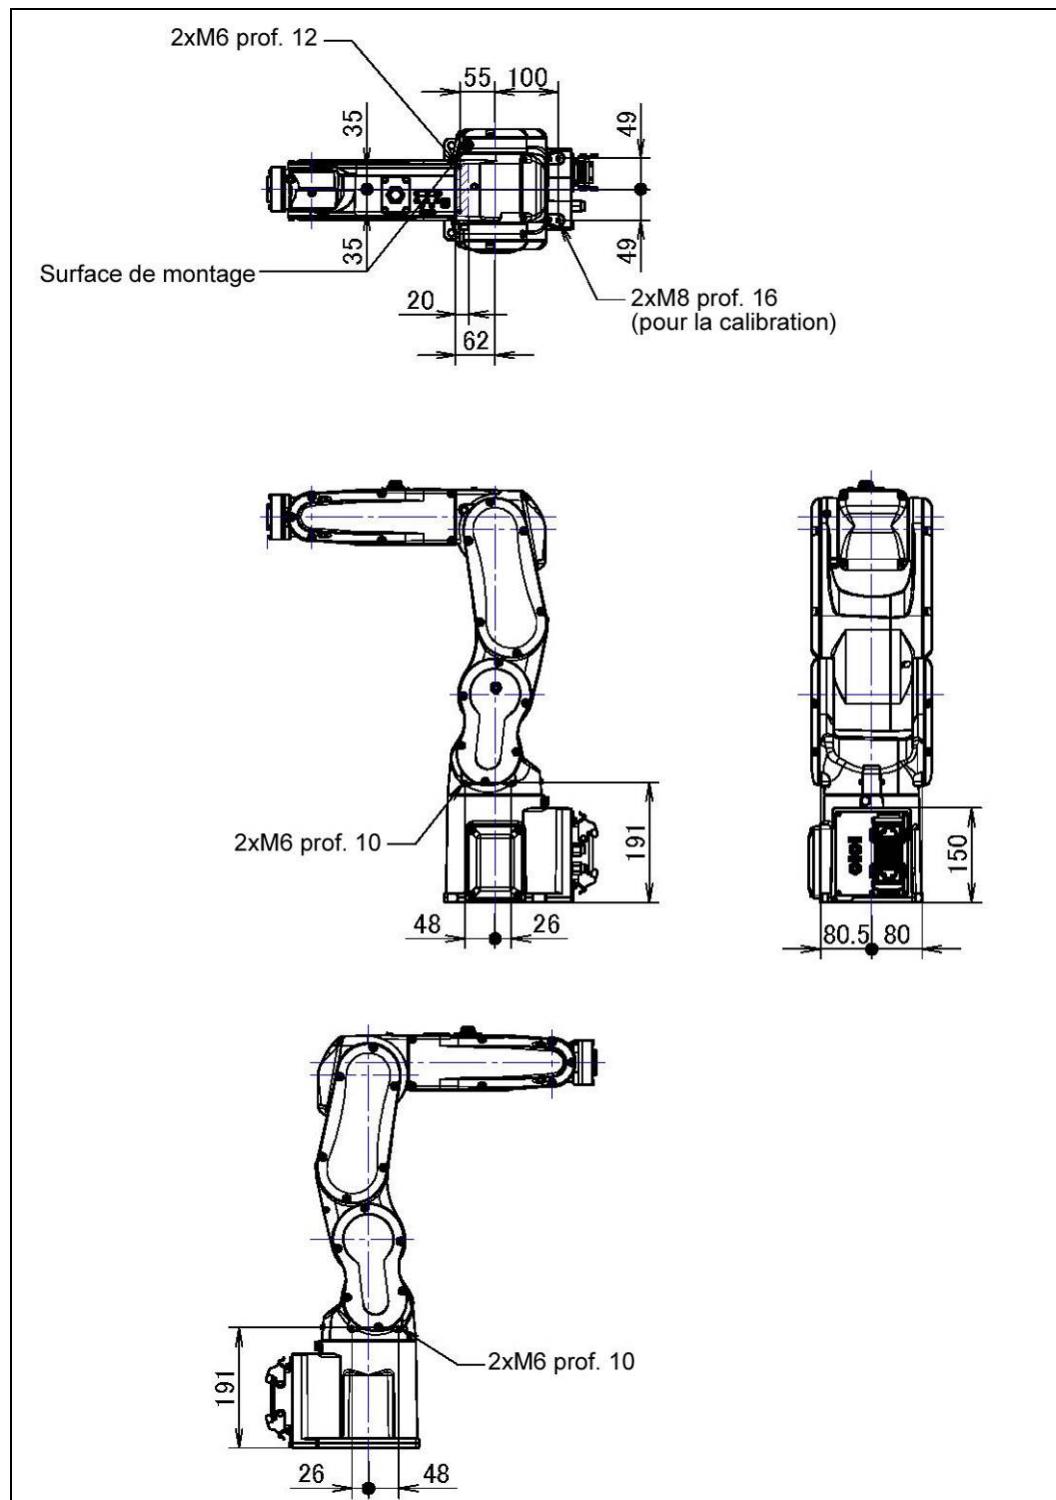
(b) Surfaces de montage d'équipement (LR Mate 200iD/4S)
